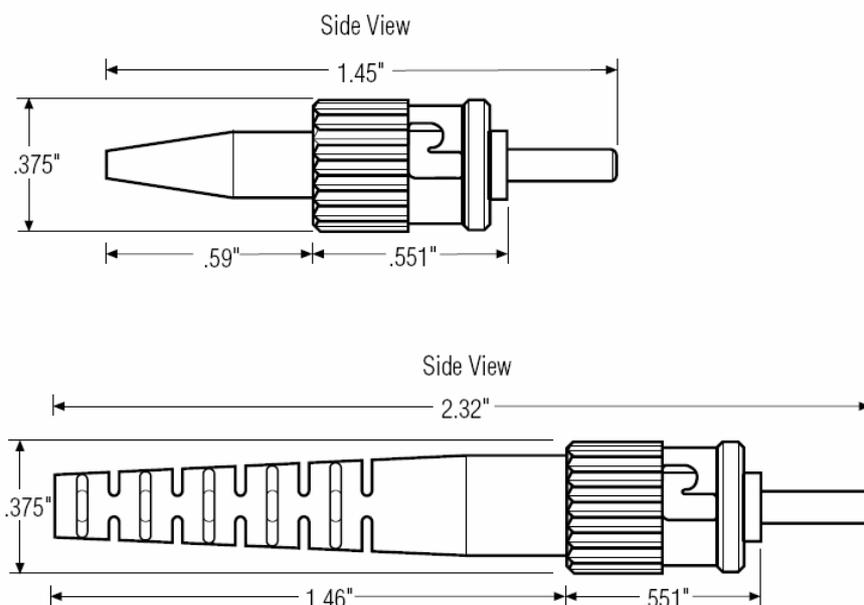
Mechanische Abmessungen des optischen Steckers ST
